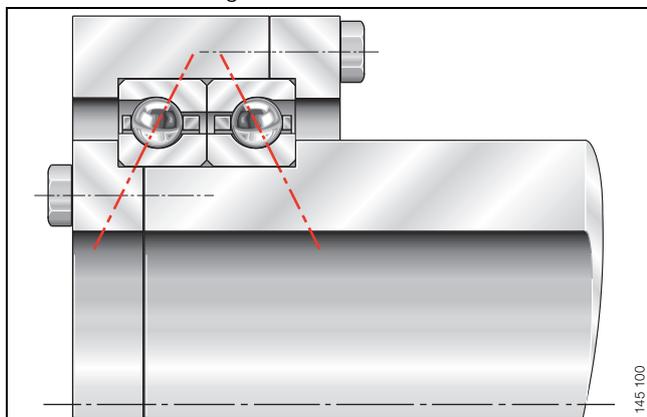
· Zusammengepasste Schrägkugellager, O-Anordnung
